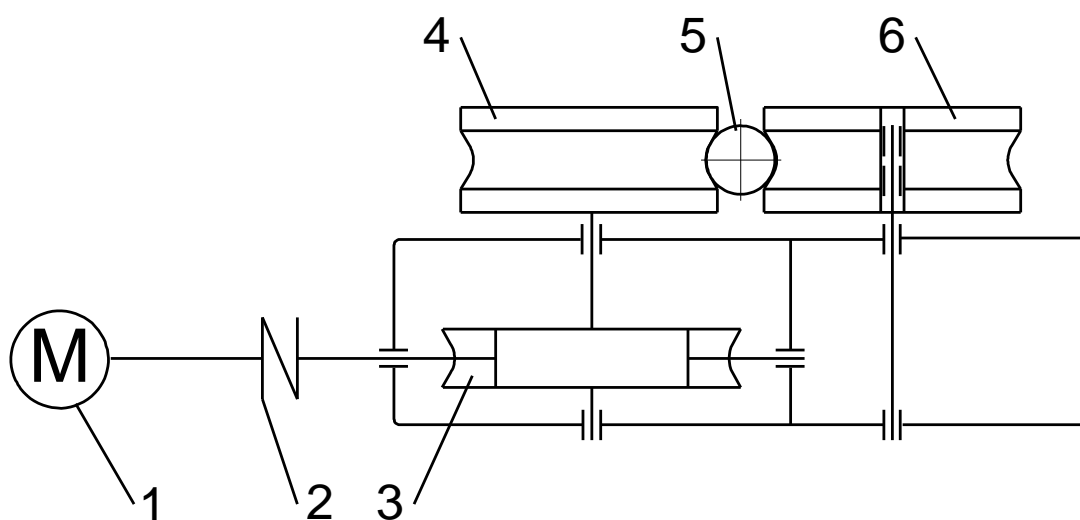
Кинематическая схема механизма выталкивания заготовок:
